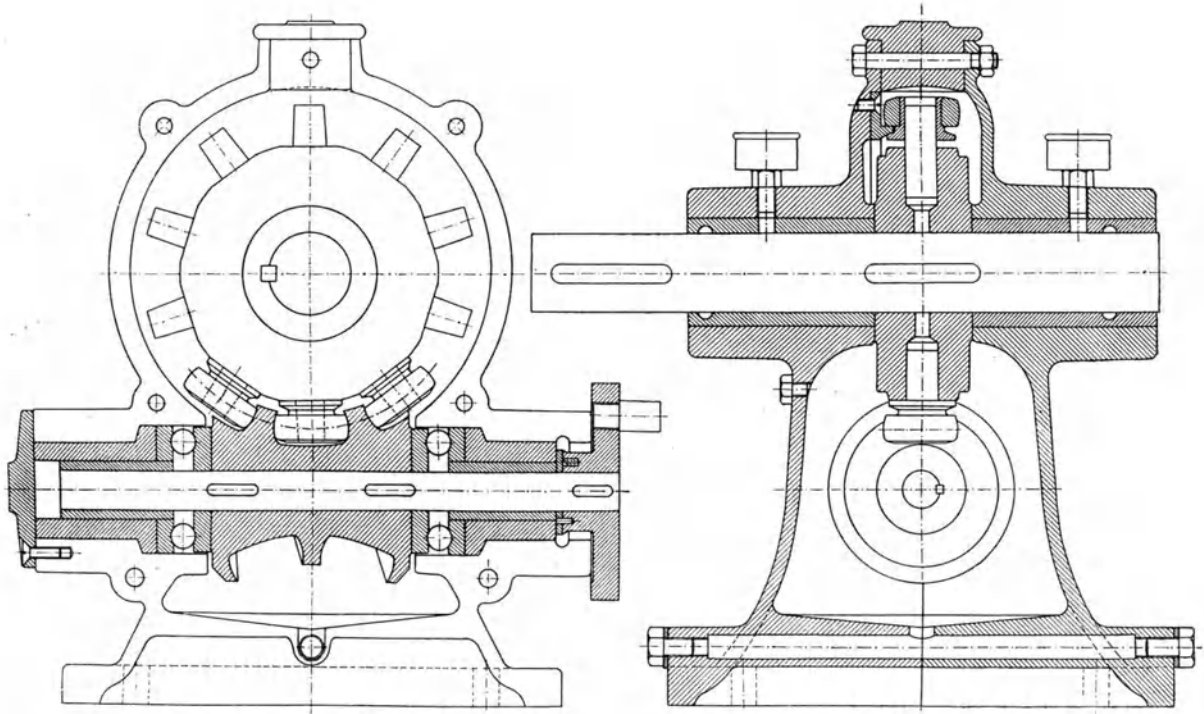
Ausführung der Maschinenfabrik Pekrun, Coswig.
